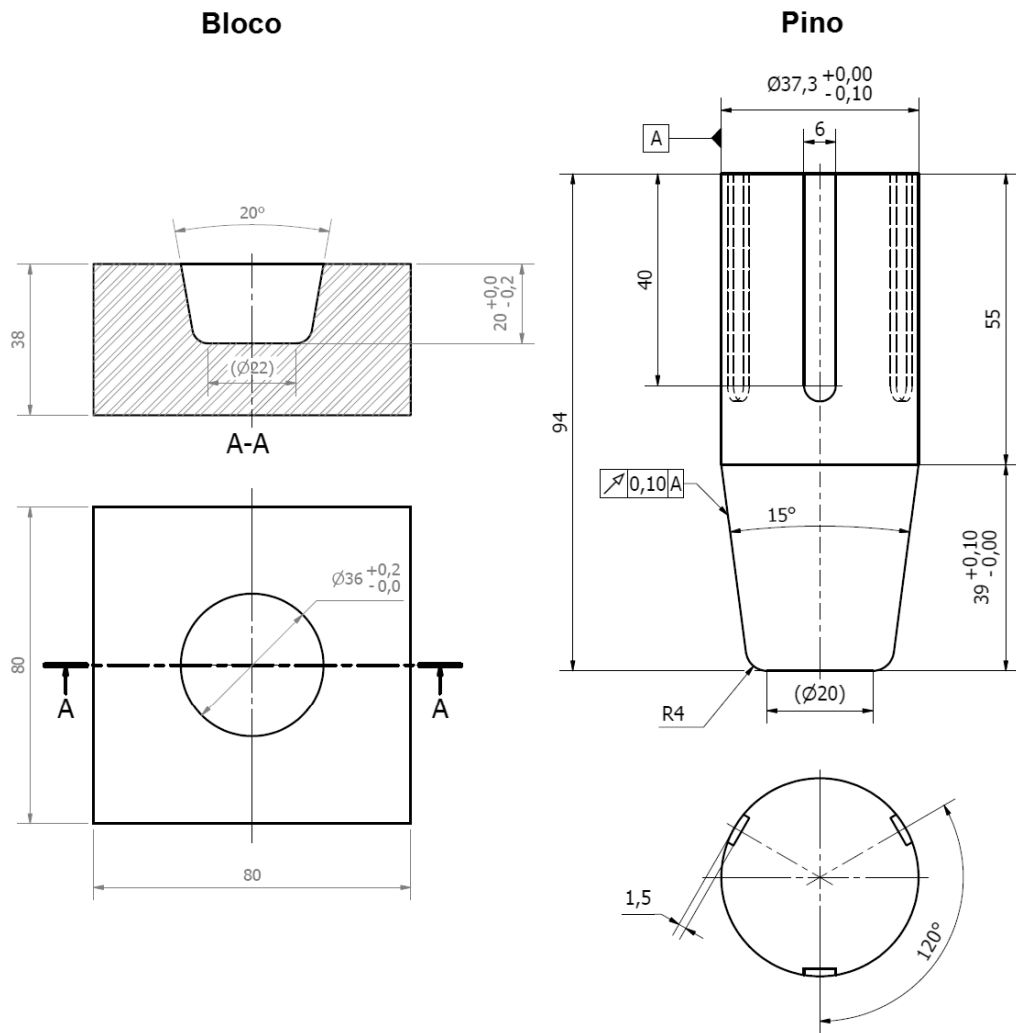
Dimensões do pino e do bloco da geometria “C” (cotas em mm)
